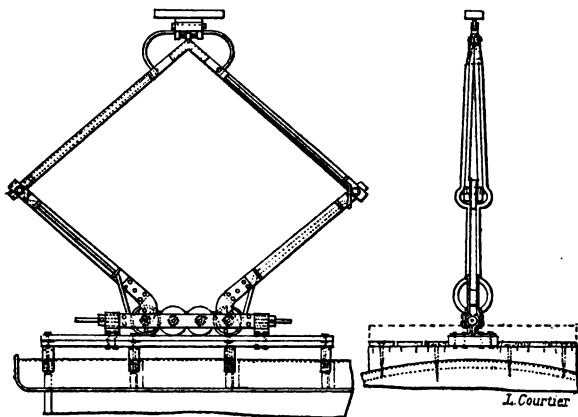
et 8. — Vue latérale et vue en bout du trôlet.
